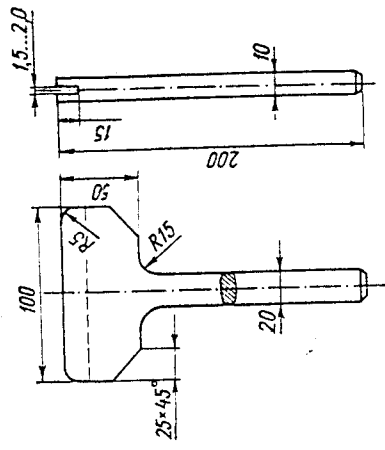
Оправка для установки уплотняющих прокладок в пазы статора
